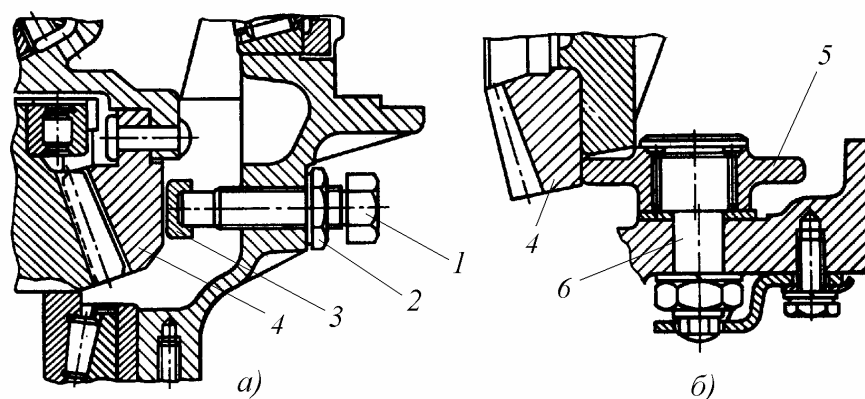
Установка упора конического колеса центральной (главной) передачи:
